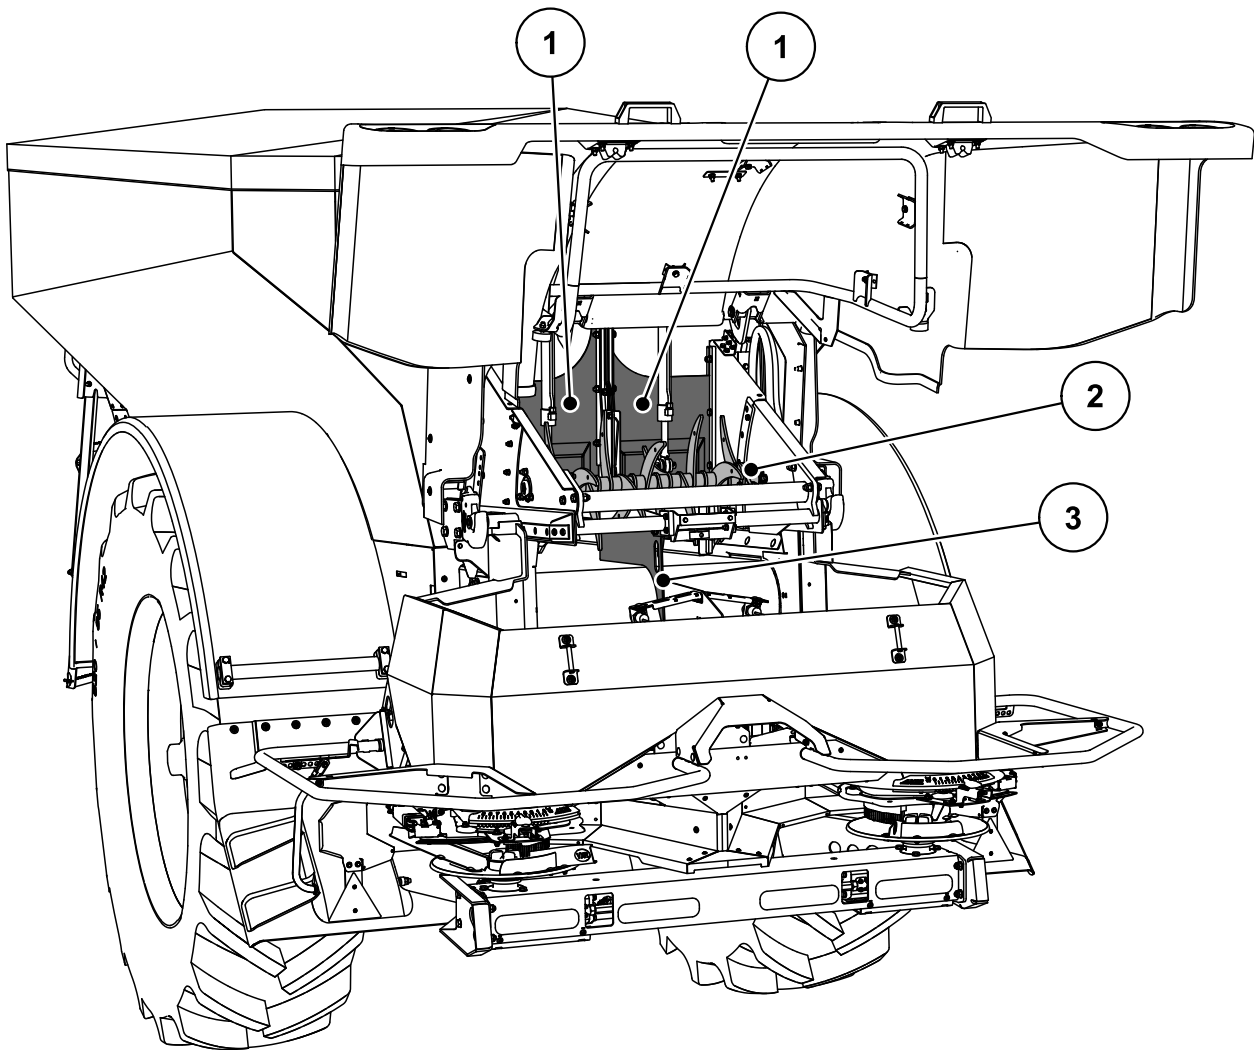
Composants et fonctionnement de la machine AXENT, vue arrière
